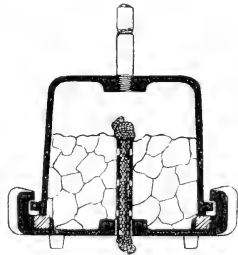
Vorrichtung zur Acetylengas-erzeugung an der französischen Fanglampe.
